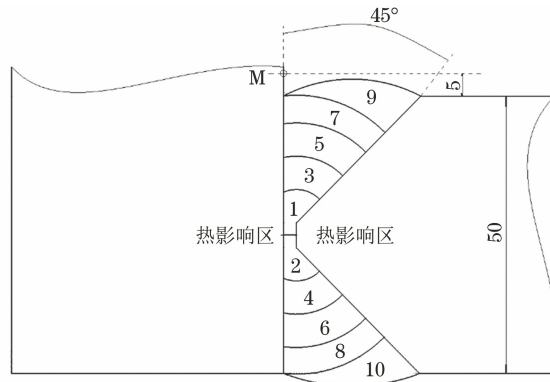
接头I处的V型坡口尺寸和焊接顺序
